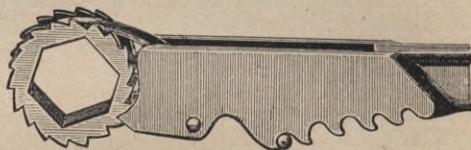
„Rapid“-Schraubenschlüssel mit eingesehter Nut.
